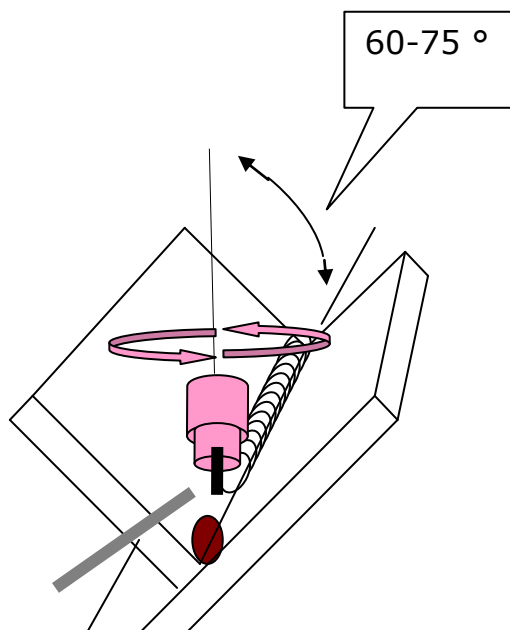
Realización del cordón en posición plana de juntas a filetes, en placas.
